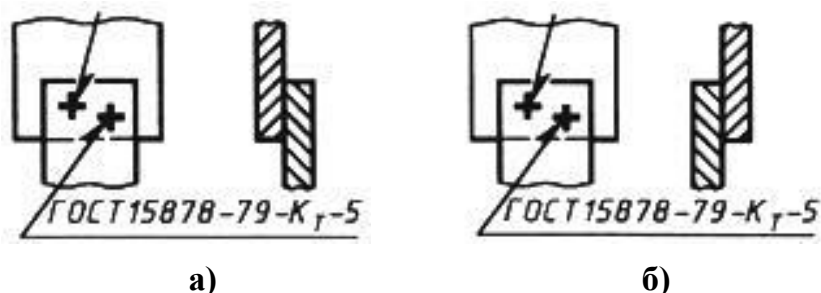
Пример обозначения сварного шва [5]: а – обозначение с лицевой стороны; б – обозначение с оборотной стороны
